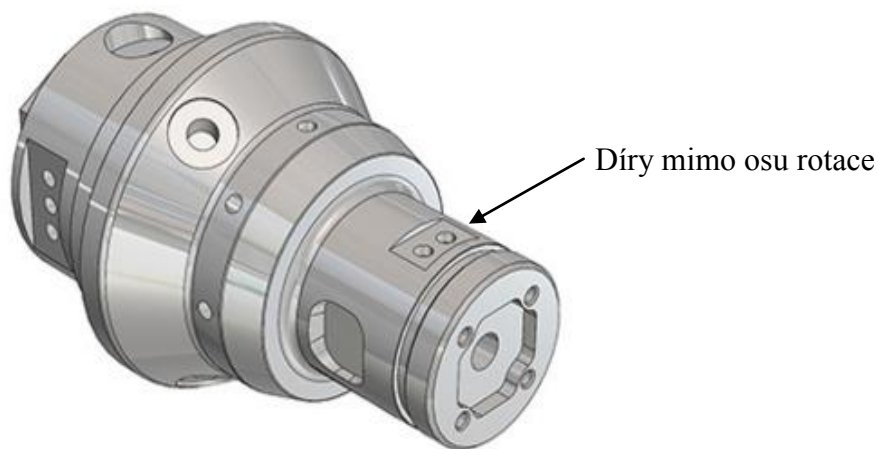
Praktická ukázka výrobku s radiálním vrtáním
